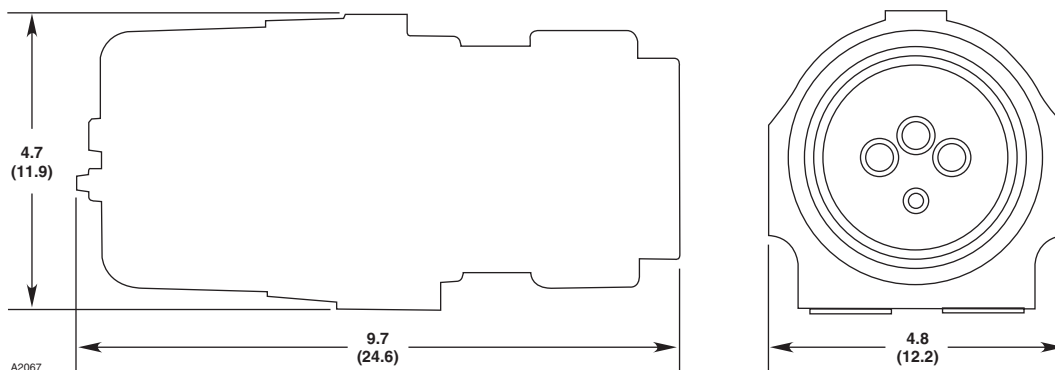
Abmessungen des X3301 in Zoll (cm)
